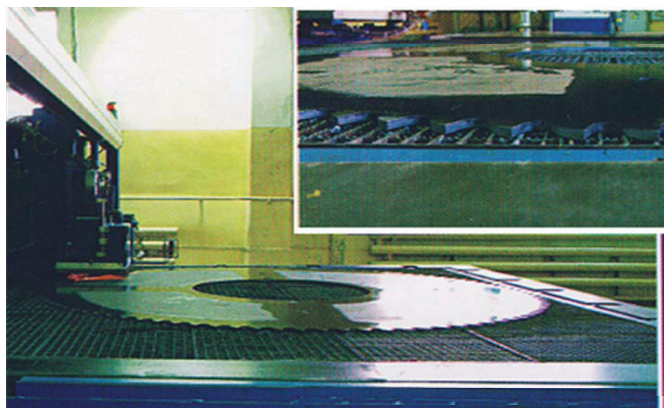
Диски для роторных пил горячей резки металла (диаметр 2500 мм, толщина 12 мм)
